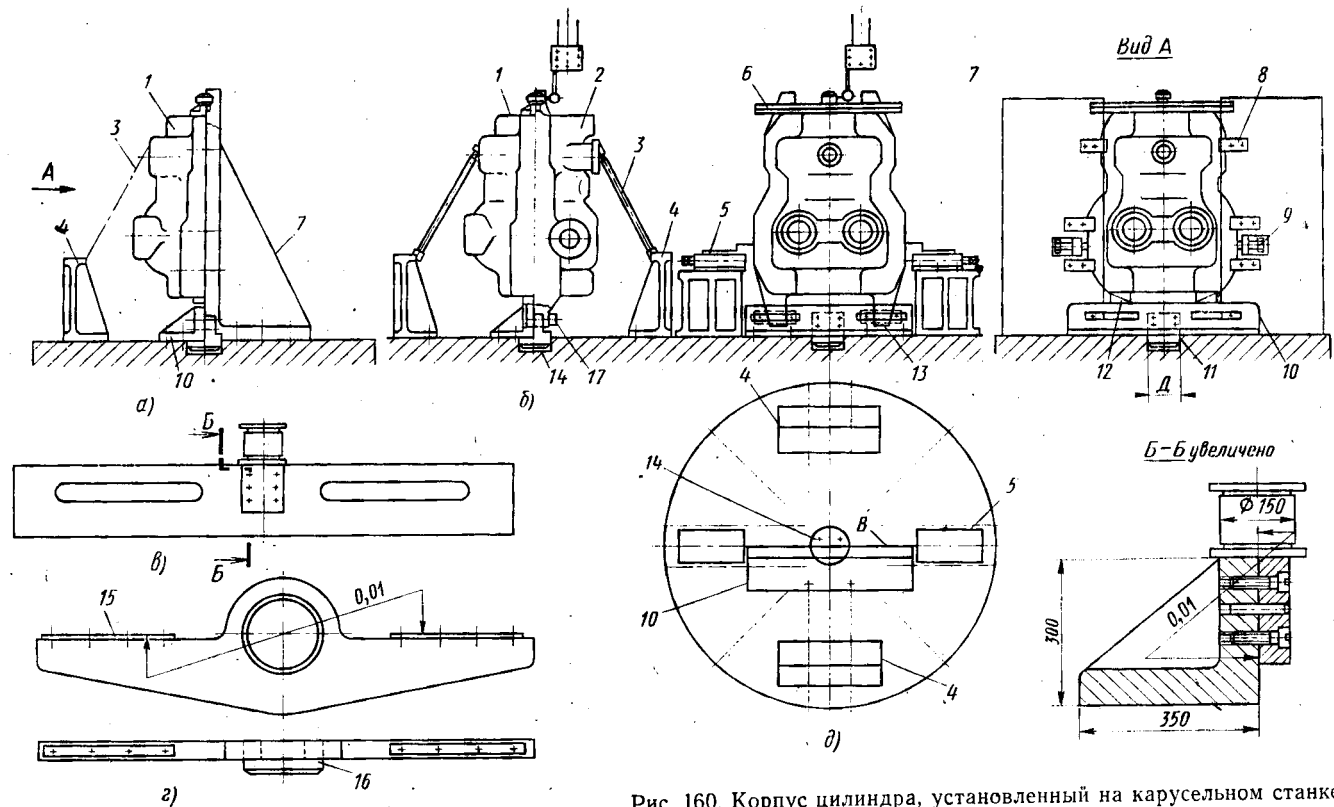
Корпус цилиндра, установленный на карусельном станке:
